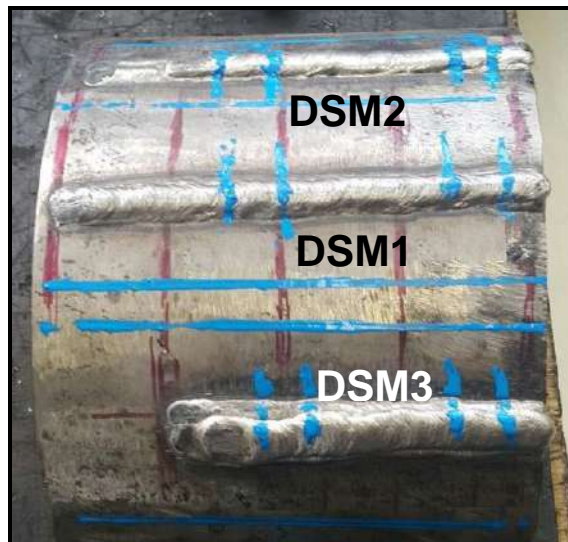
Cordões de dupla camada soldados por processo SMAW.
